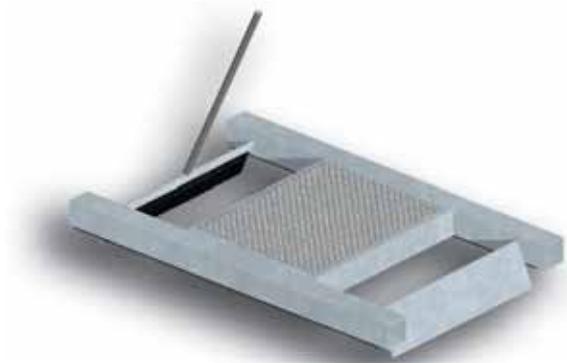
Dispositifs auxiliaires spéciaux pour panneaux de toiture
